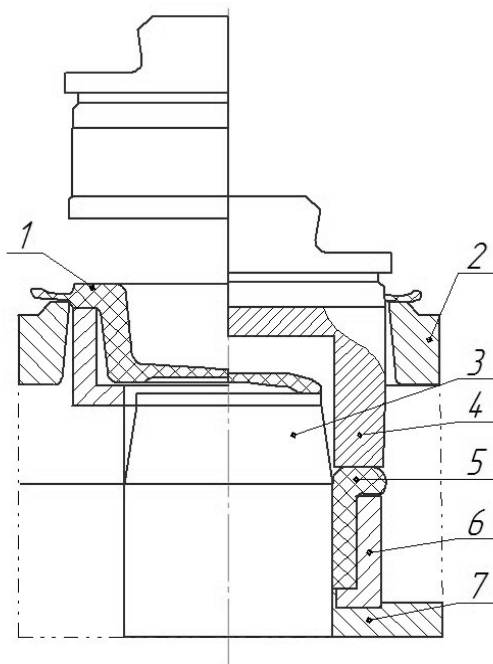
Схема штампа совмещенного действия: 1 – промежуточная заготовка, 2 – матрица, 3 – прошивень, 4 – пуансон, 5 – поковка, 6 – выталкиватель, 7 – траверса
